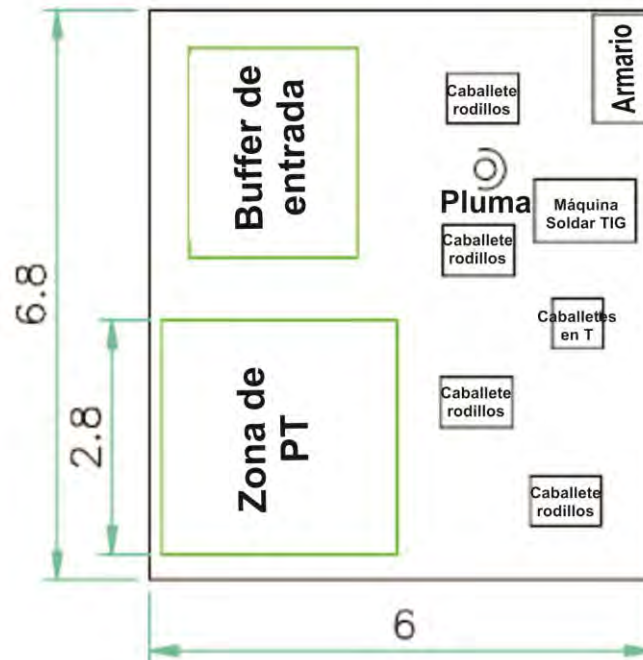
Diseño de estación de trabajo Soldadura Tridimensional – Pase de raíz
